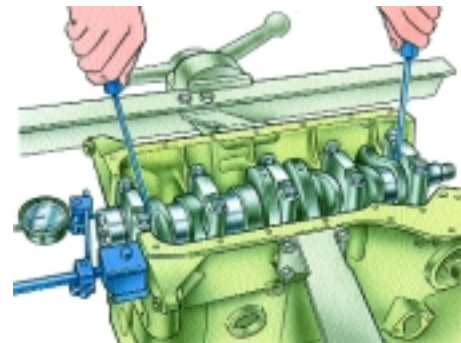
Проверка осевого зазора коленчатого вала двигателя мод. 2106–70
